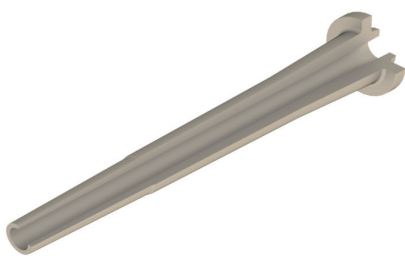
3D-модель, поковка «шпindelь металлорежущего станка»
